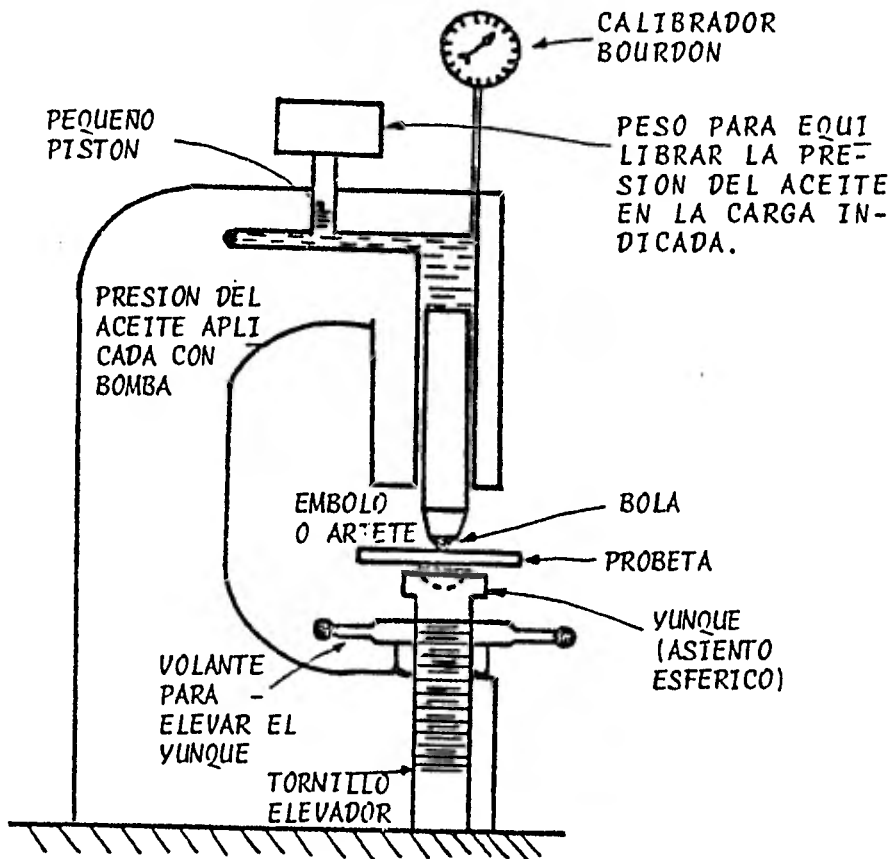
ASPECTO DE LA MAQUINA BRINELL DE TIPO HIDRAULICO.
